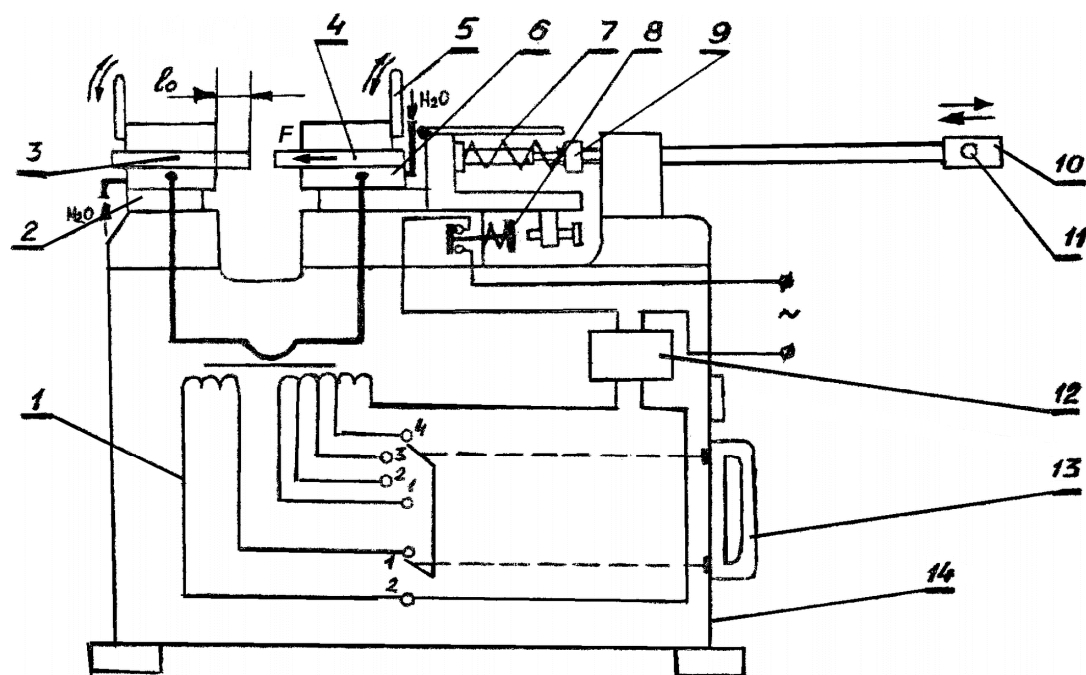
Схема машины МСР-25 для контактной стыковой сварки
